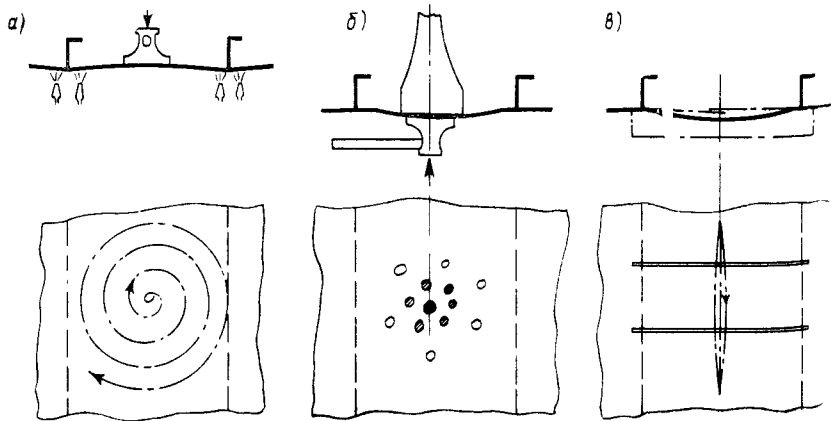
Ручная правка вмятин в сварных листах обшивки.
